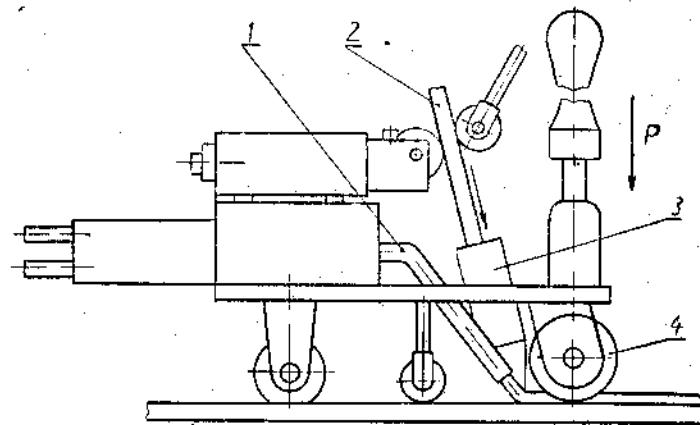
Полуавтоматическая установка для сварки пластмасс с присадочным прутом.
